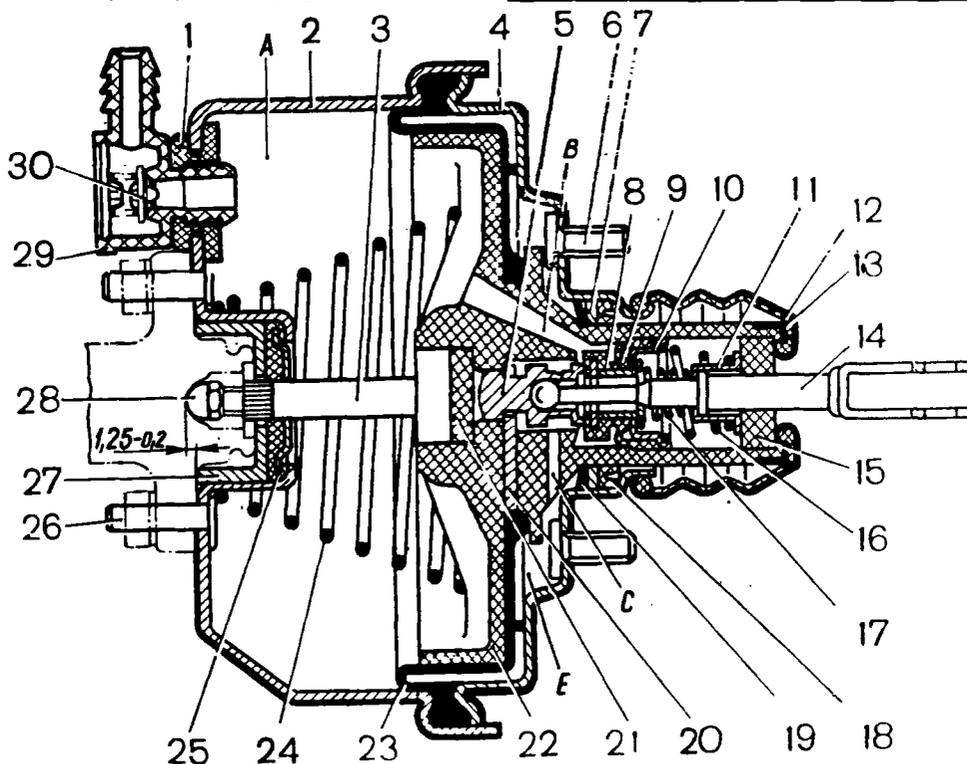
Вакуумный усилитель: 1 - фланец крепления наконечника; 2 - корпус усилителя; 3 - шток; 4 - крышка; 5 - поршень; 6 - болт крепления усилителя; 7 - дистанционное кольцо; 8 - опорная чашка пружины клапана; 9 - клапан; 10 - опорная чашка пружины клапана; 11 - опорная чашка возвратной пружины; 12 - защитный колпачок; 13 - обойма защитного колпачка; 14 - толкатель; 15 - воздушный фильтр; 16 - возвратная пружина клапана; 17 - пружина клапана; 18 - уплотнитель крышки корпуса; 19 - стопорное кольцо уплотнителя; 20 - упорная пластина; 21 - буфер; 22 - корпус клапана; 23 - диафрагма; 24 - возвратная пружина корпуса клапана; 25 - уплотнитель штока; 26 - болт крепления главного цилиндра; 27 - обойма уплотнителя штока; 28 - регулировочный болт; 29 - наконечник шланга; 30 - клапан. А - вакуумная полость; В - канал, соединяющий вакуумную полость с внутренней полостью клапана; С - канал, соединяющий внутреннюю полость клапана с атмосферной полостью; Е - атмосферная полость
